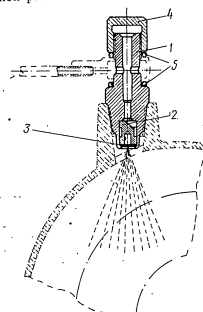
Заливочная форсунка. 1—корпус форсунки, 2—завихритель, 3—распылитель, 4—колпачок, 5—прокладка.
